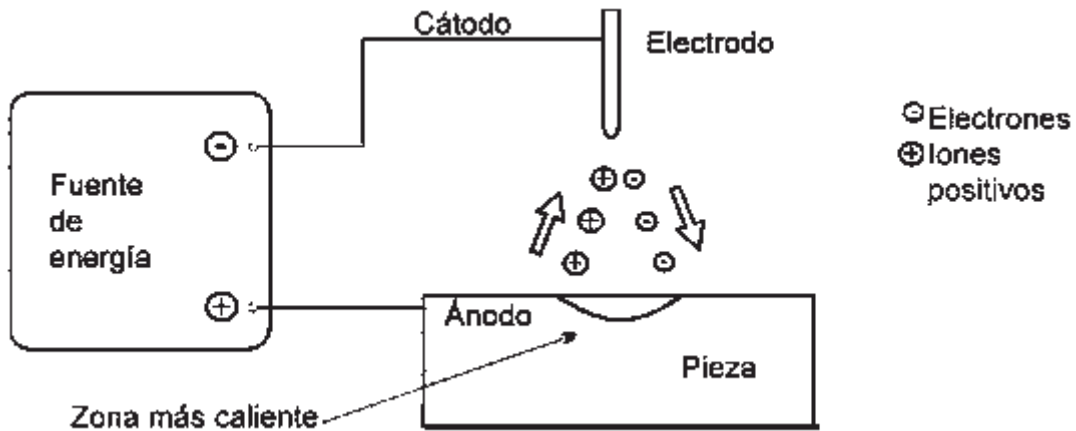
Uso de la polaridad directa en soldadura del aluminio
